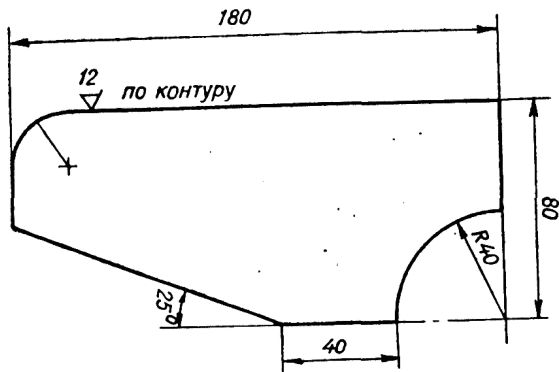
Креслення деталі (планка АП. 3.100.01), призначеної для обробки на верстаті з ЧПУ.
